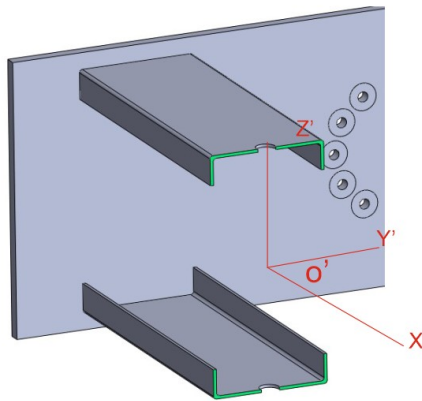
Corte en la sección o' del soporte móvil con SR.
